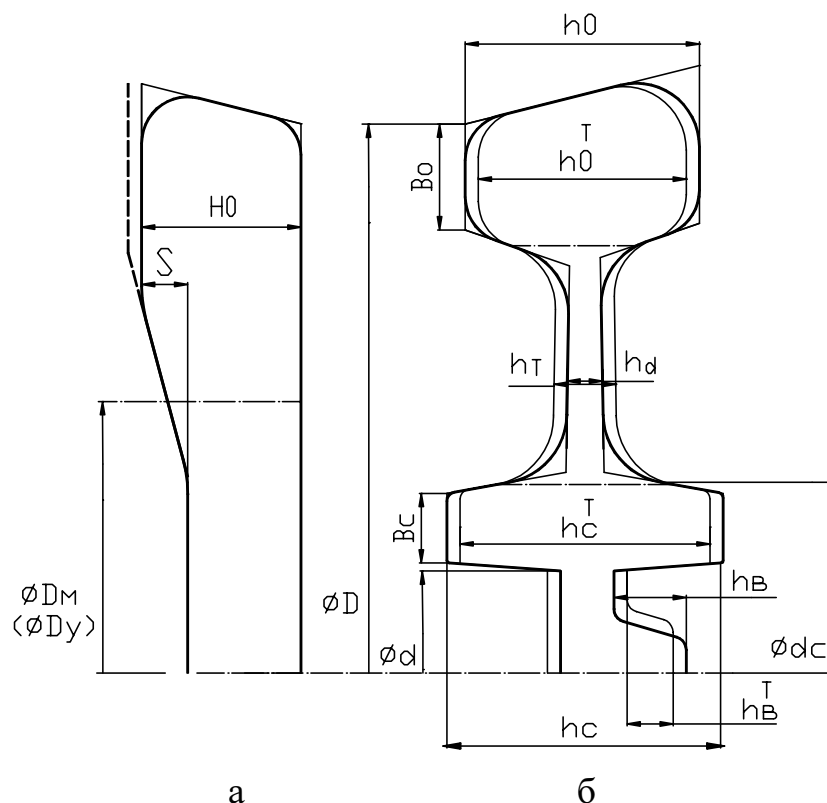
Схемы заготовок: а – после разгонки конусной плитой на прессе силой 50 МН; б – после формовки в штампах прессы силой 100 МН
